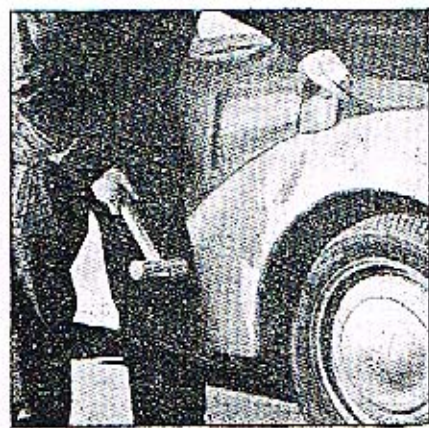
Ohlů „pěst“ k podložení při vyrovnávání poškozeného blatníku
